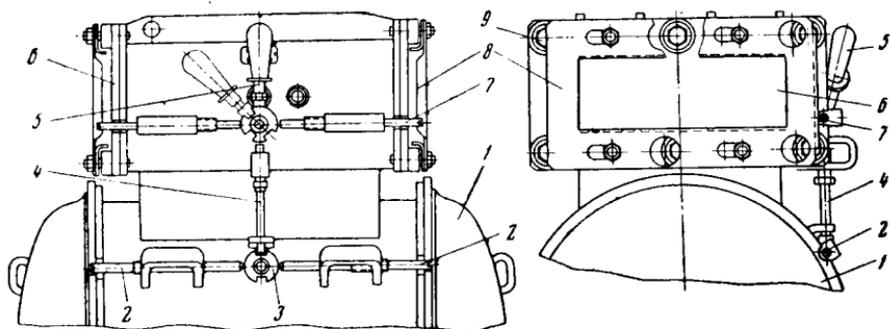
Блокировочное устройство реверсора РКВ-300
